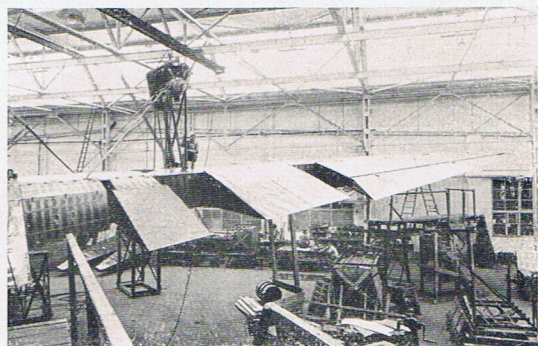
Réservoirs et caisson de profilage fixés au caisson central d'aile
